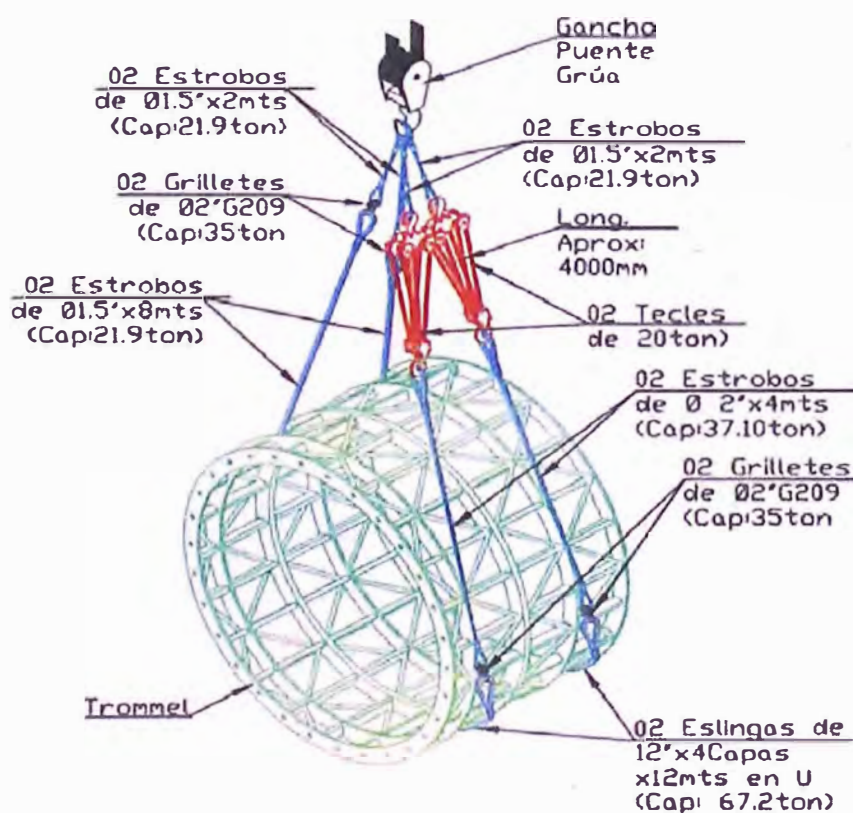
Detalle y elementos de izaje para el montaje del trommel de descarga del molino Sag.
